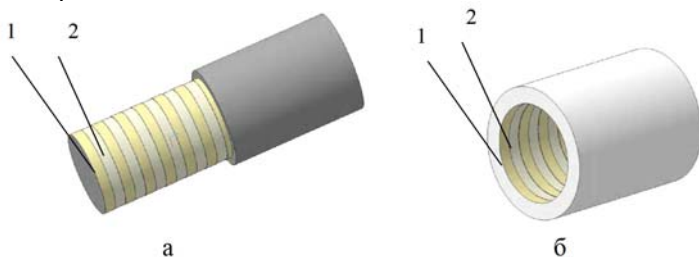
Поверхности вала (а) и втулки (б) с кольцевыми участками электроэрозионных покрытий: 1 - твердым сплавом группы ВК или ТК; 2 – никелем.
